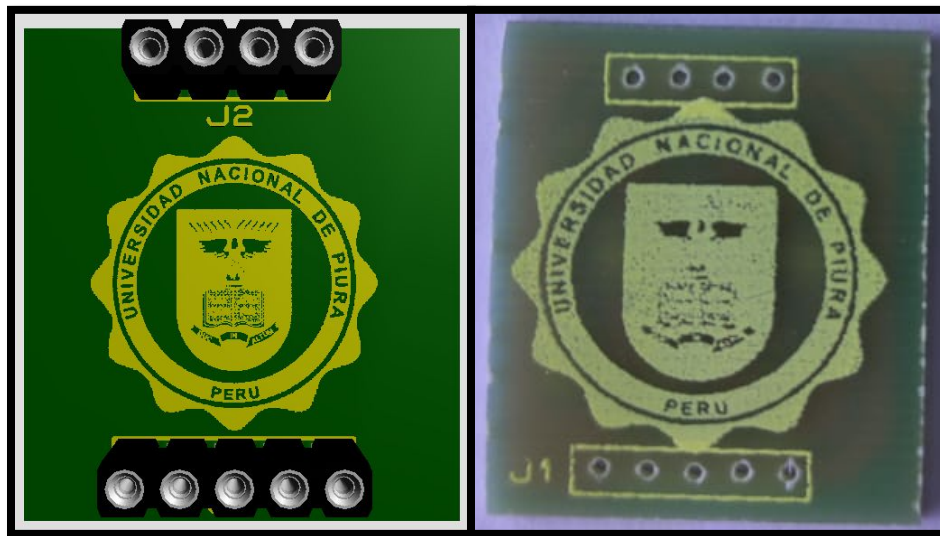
Diseño PCB del lado BOTTOM del interruptor lógico.
